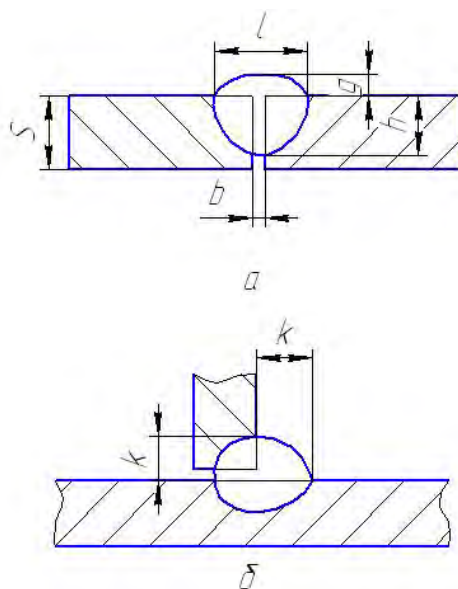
Основные геометрические параметры сварных швов:
